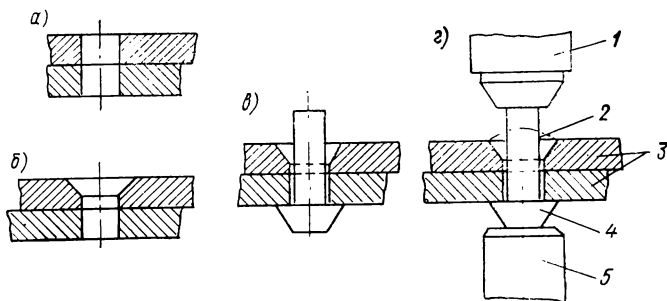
Схема технологического процесса ручной пневматической клепки: а — развернутое отверстие; б — раззенковка под замыкающую головку; в — подача стержня заклепки в отверстие; г — расклепывание стержня.
